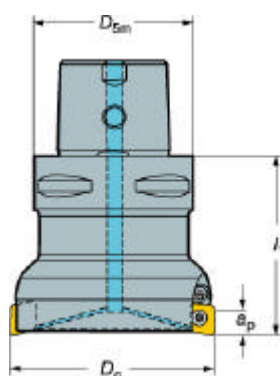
Fresa com corpo em alumínio para maquinagem de alumínio¹
